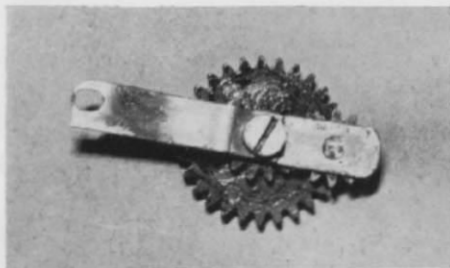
Der neue Getriebe- bzw. Zahnradsatz in zusammengebautem Zustand, wie er am Motorblock angeschraubt wird.
